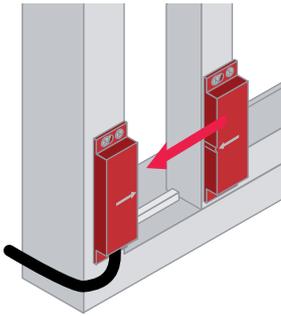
Die Markierungen fluchten auf gleicher Ebene.
